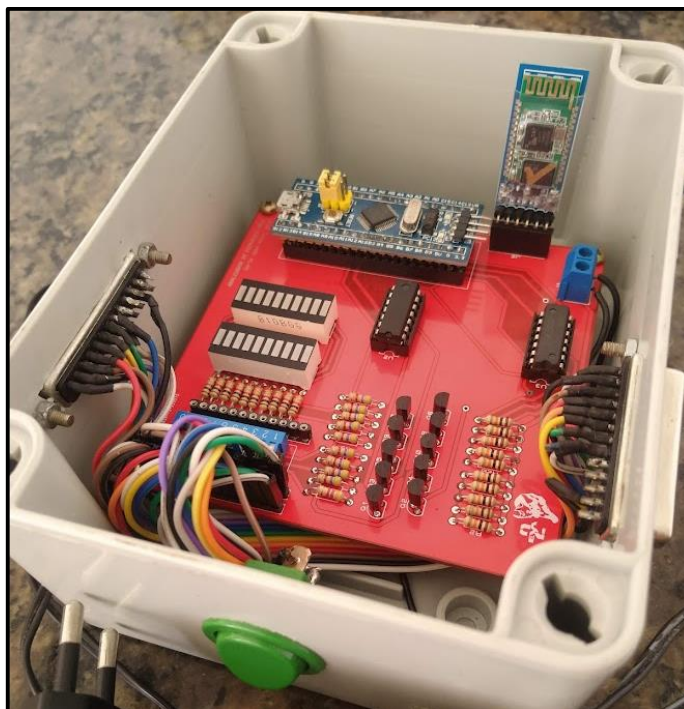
Soldagem dos componentes, soquetes e fixação de módulos na PCB.
